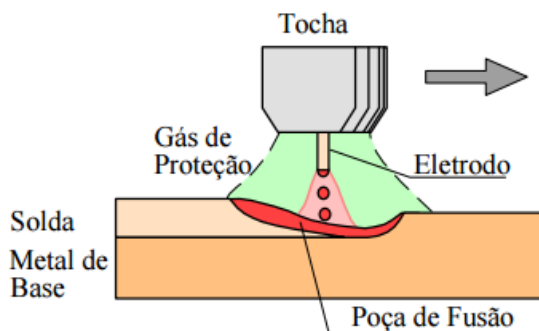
Desenho esquemático da soldagem GMAW (Marques 2009)
